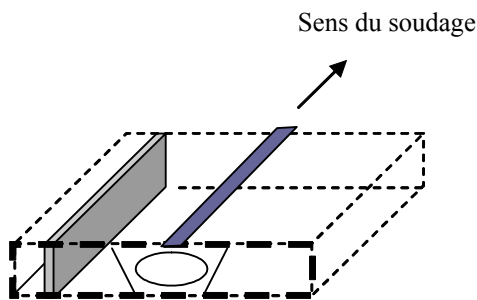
Dimensionnement d'une éprouvette macroscopique prélevée perpendiculairement à la direction de soudage. La zone grise représente la soudure
